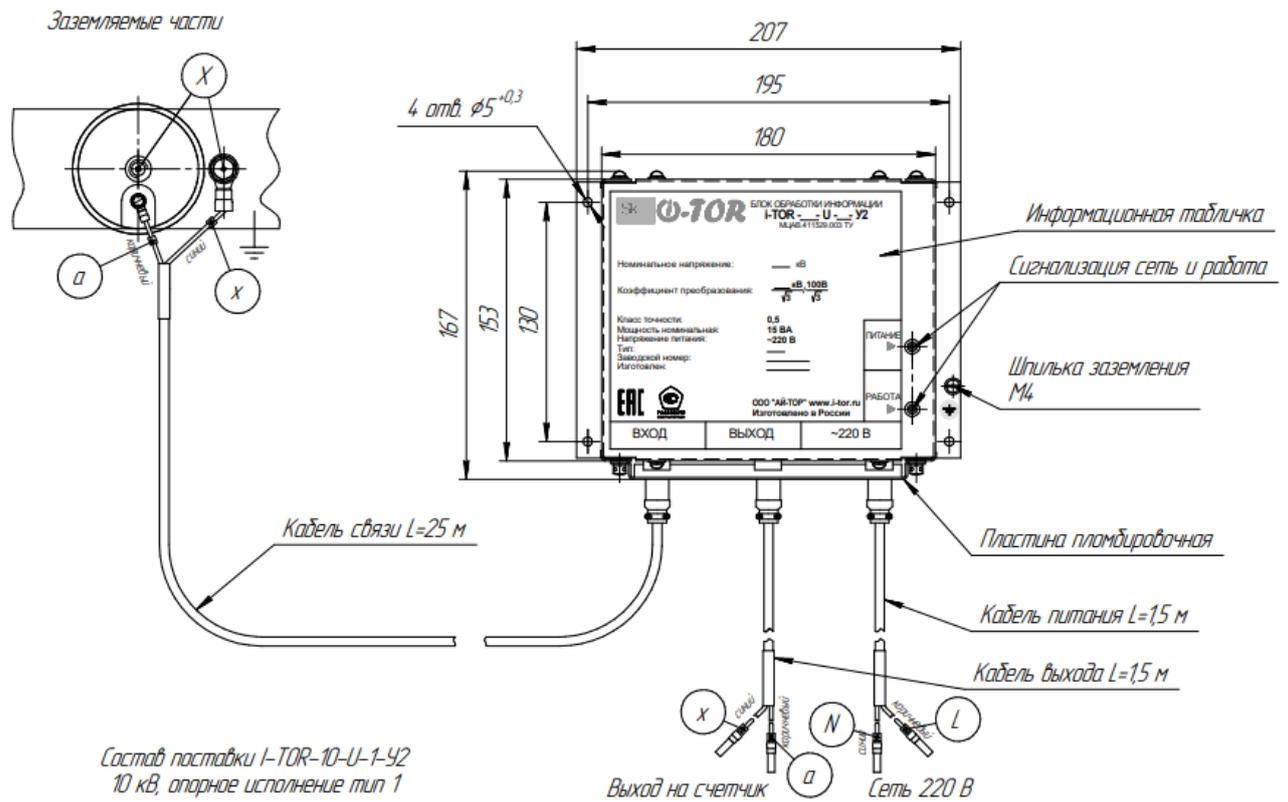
Габаритно-присоединительные размеры компонентов устройств для измерения напряжения типа I-TOR..
